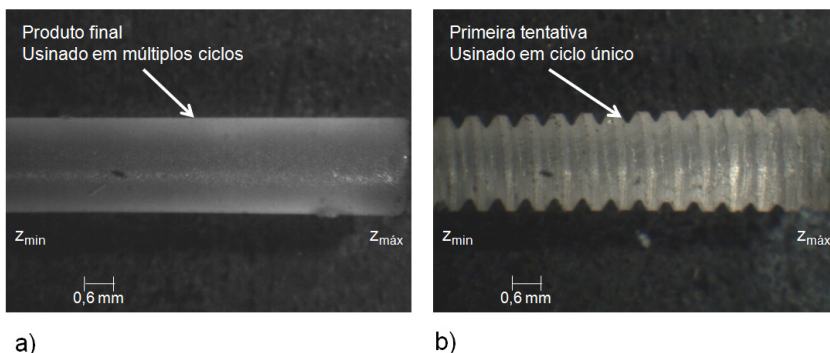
Imagens estereoscópicas das geometrias usinadas nas diferentes metodologias utilizadas. a) Geometria usinada em múltiplos ciclos de usinagem, com relação $L/\varnothing \leq 3,5$. b) Geometria usinada em ciclo único, com relação $L/\varnothing = 4,5$.
